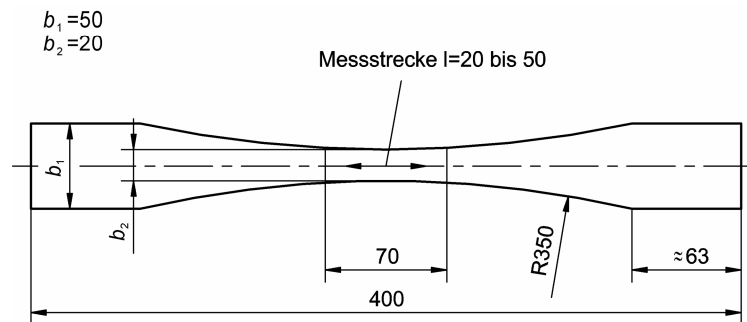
Geometrie einer Sperrholz-Zugprobe /DIN78b/
